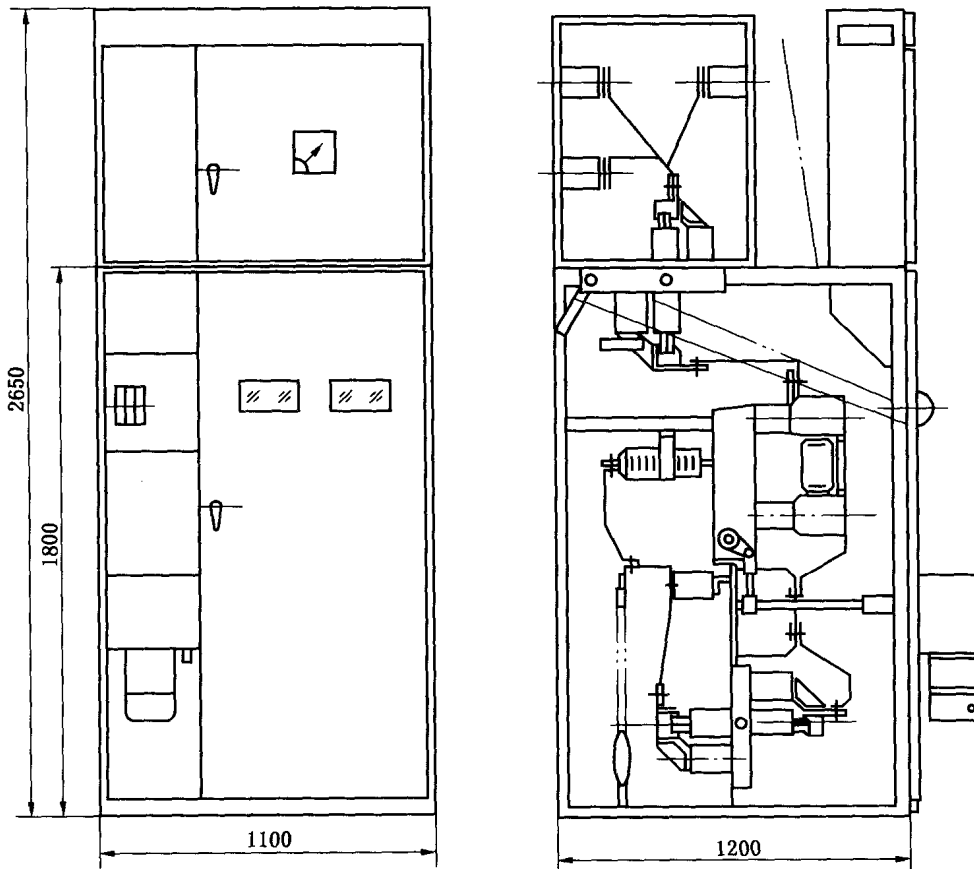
XGN□-10Z 型固定式金属封闭高压开关柜外形尺寸 (mm)
